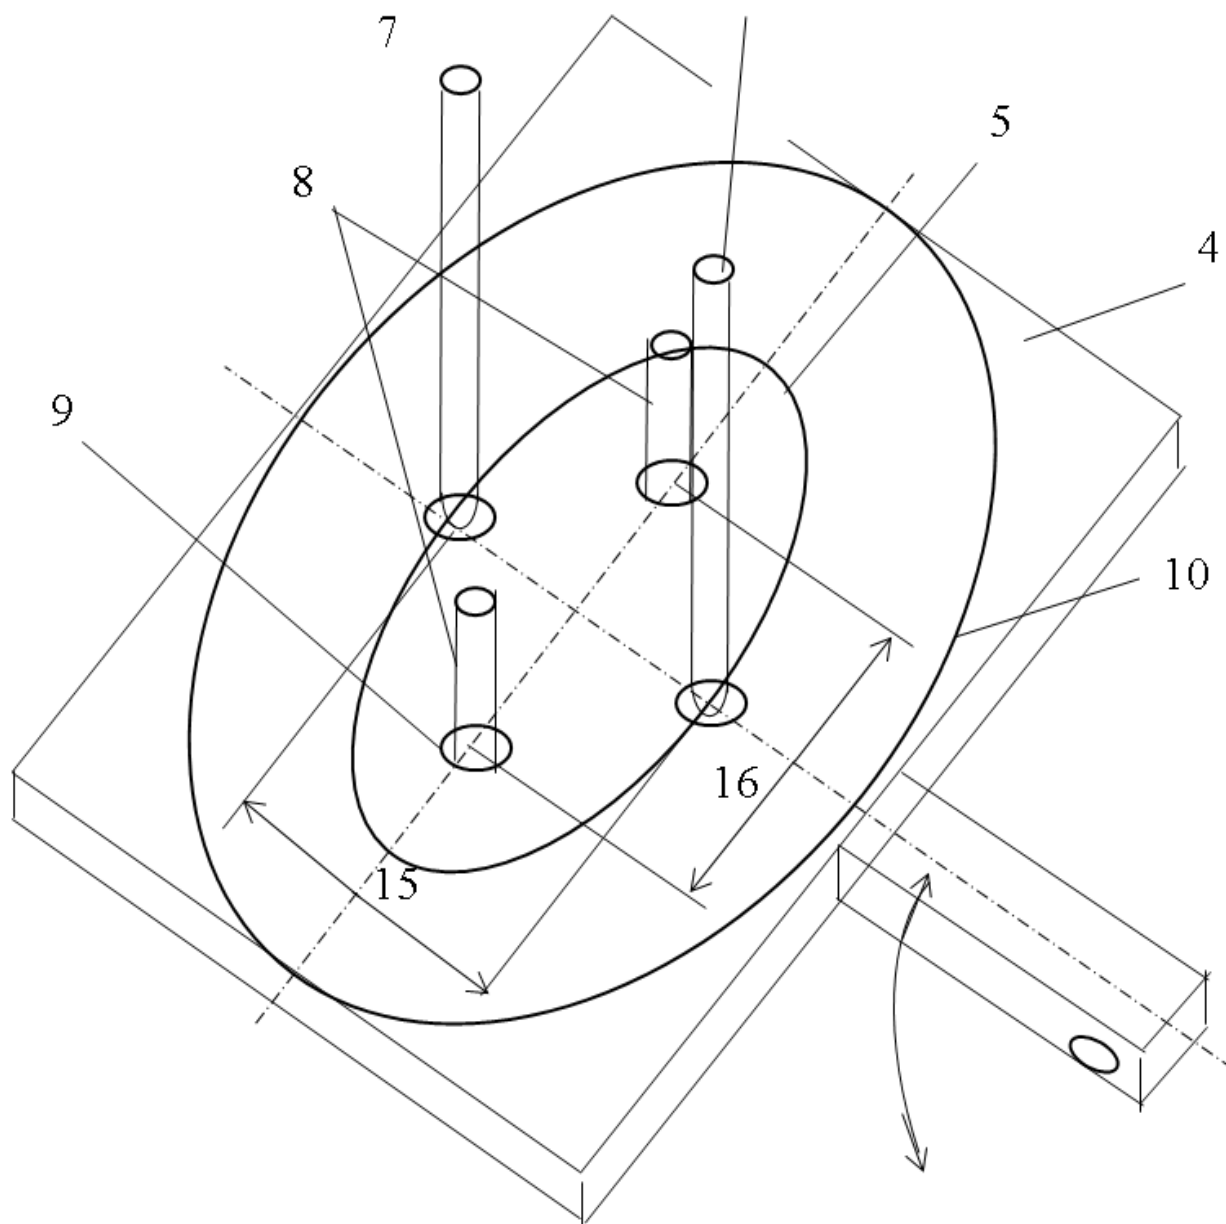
Подъемно-поворотное стусло измерительного кондуктора:
